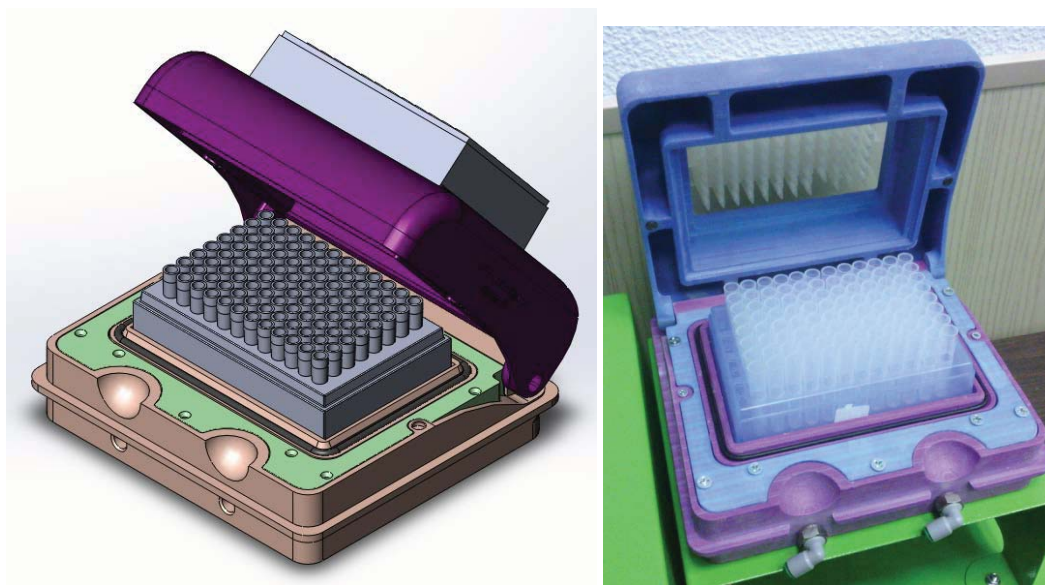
Модель блока вакуумной сепарации с магнитным соединением (слева) и изготовленный его прототип (справа)
